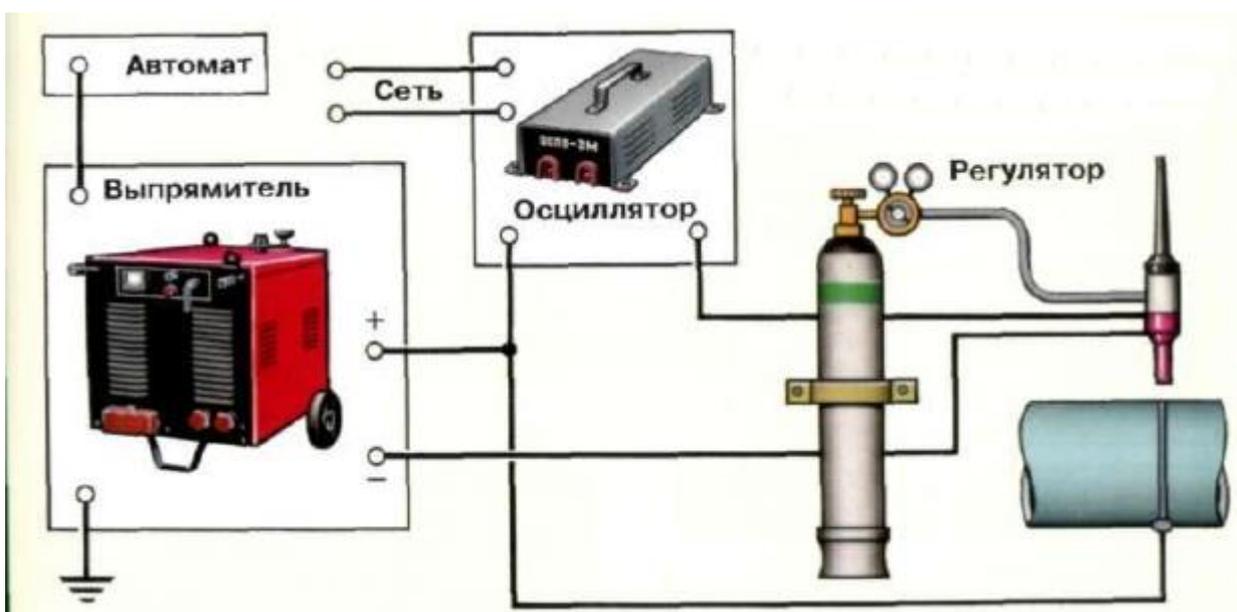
Сварка неплавящимся электродом в защитном газе
